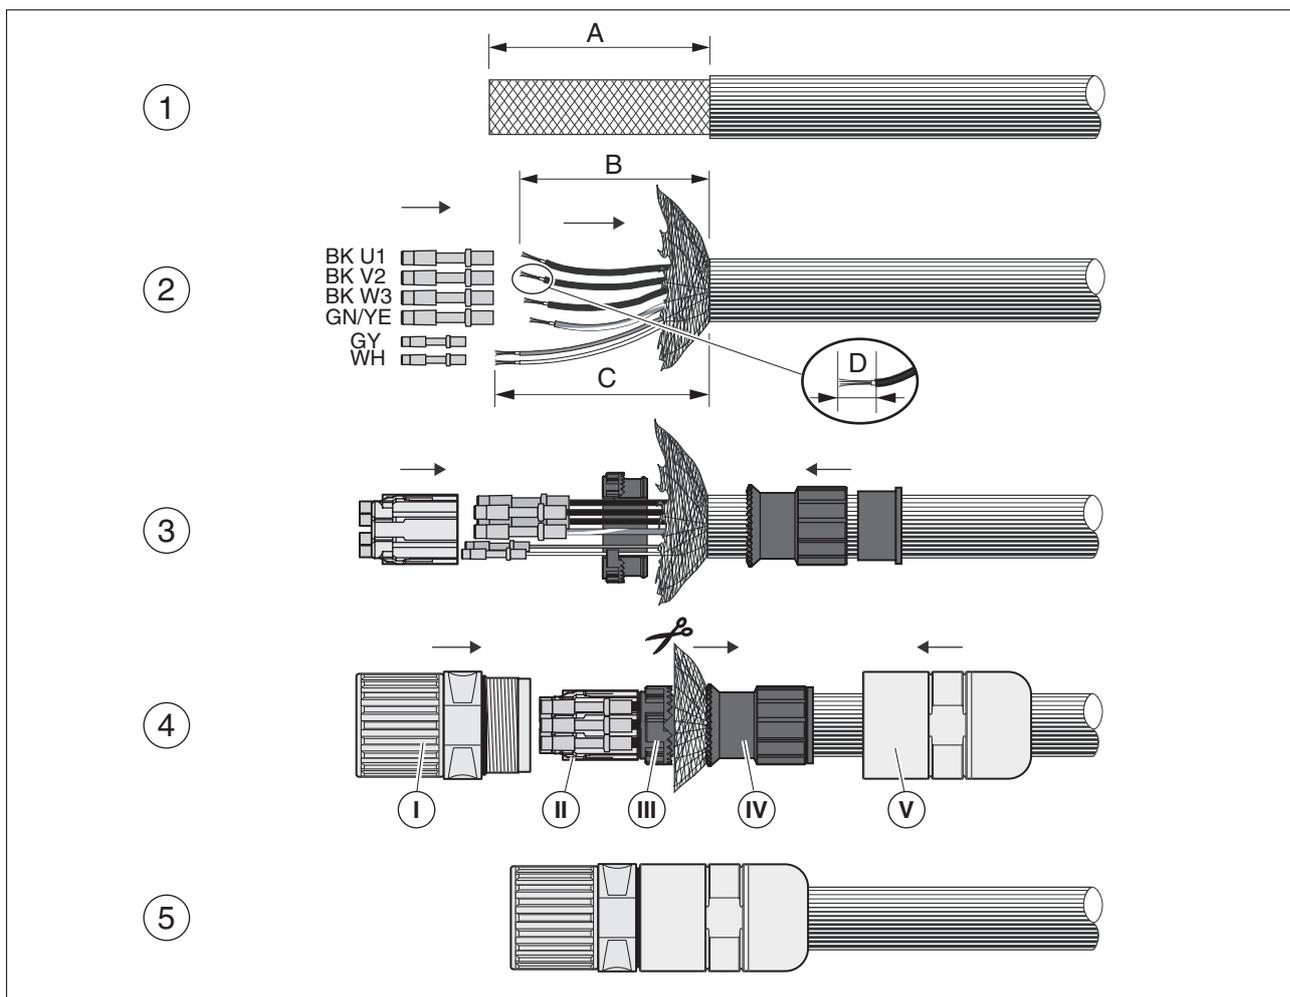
Assemblare il cavo motore con connettore motore M23
